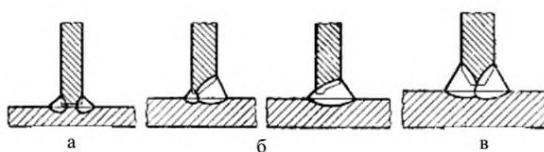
Подготовка кромок угловых швов тавровых соединений: а - без разделки кромок; б, в - с разделкой кромок
